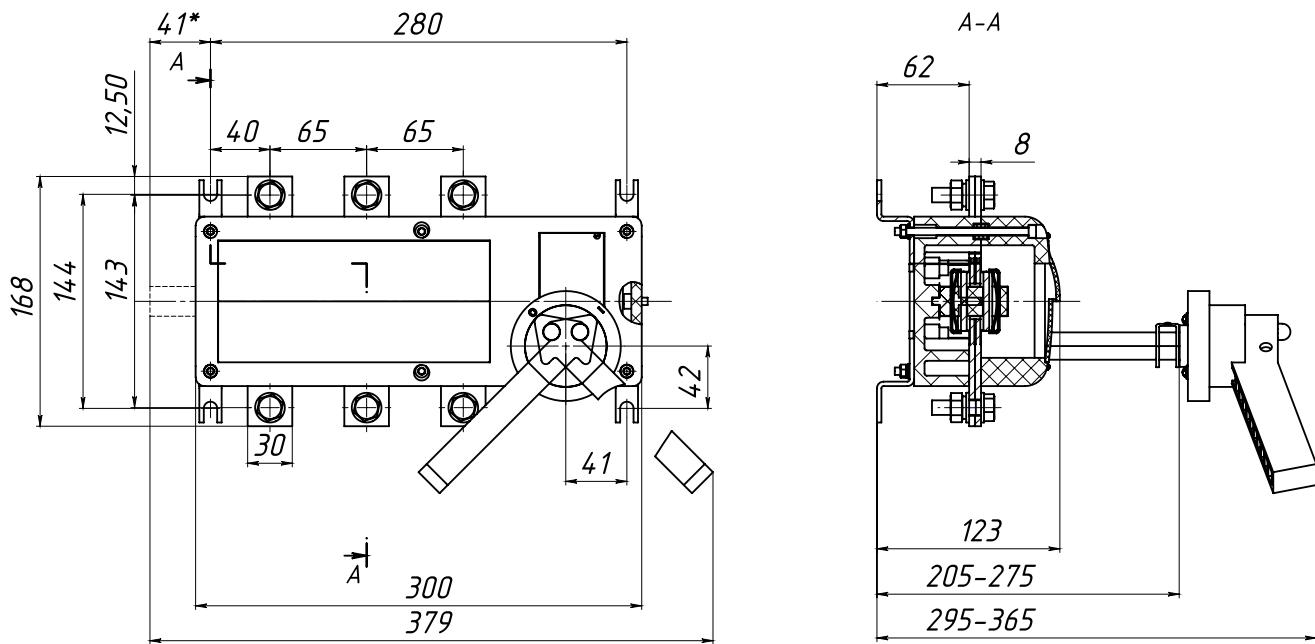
Выключатель-разъединитель ВНК-37-31130-32 УХЛЗ
